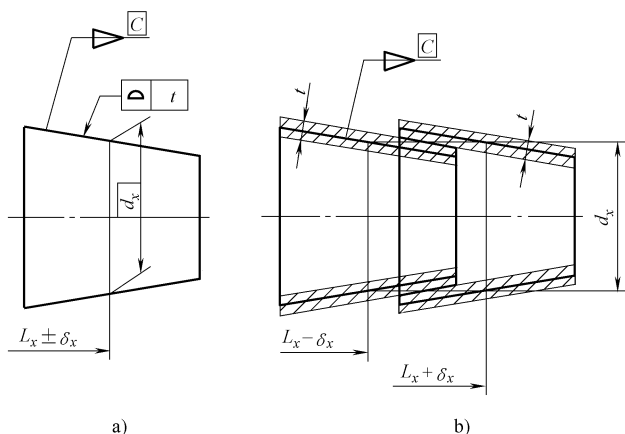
给定圆锥轴向位置的尺寸公差标注
